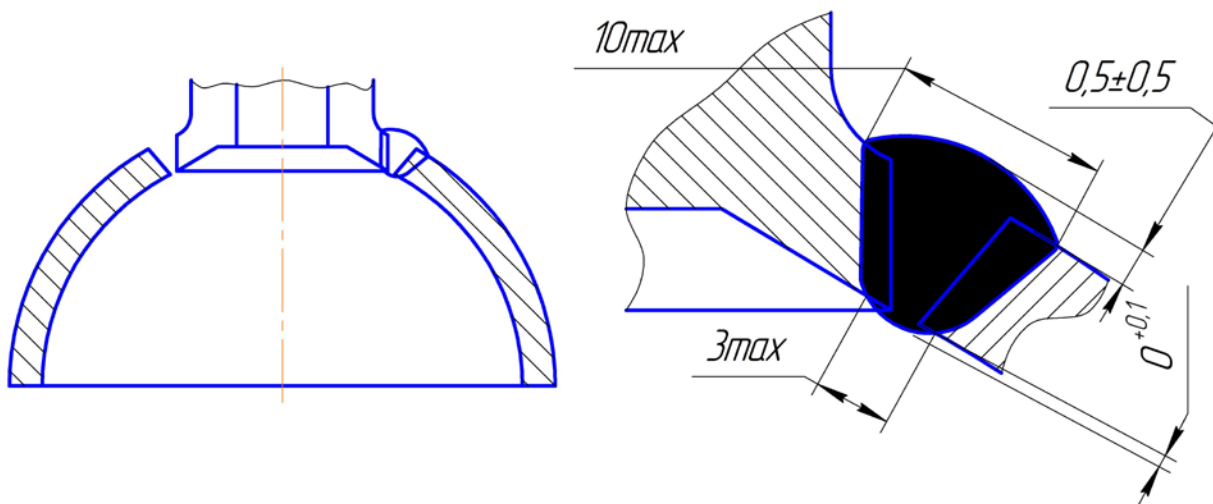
Эскиз сварного соединения узлов №1 и №2
